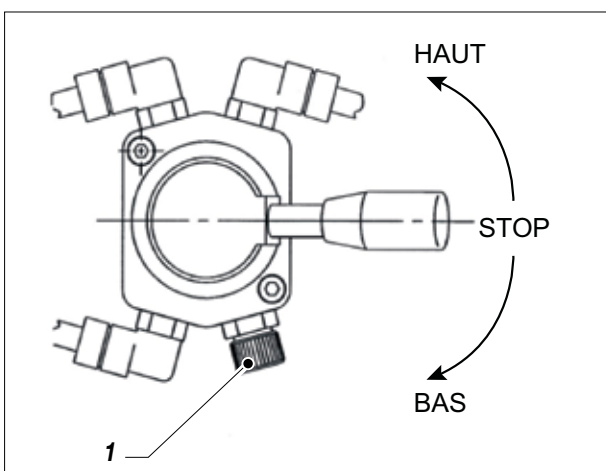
Réglage de la vitesse du cylindre pneumatique
